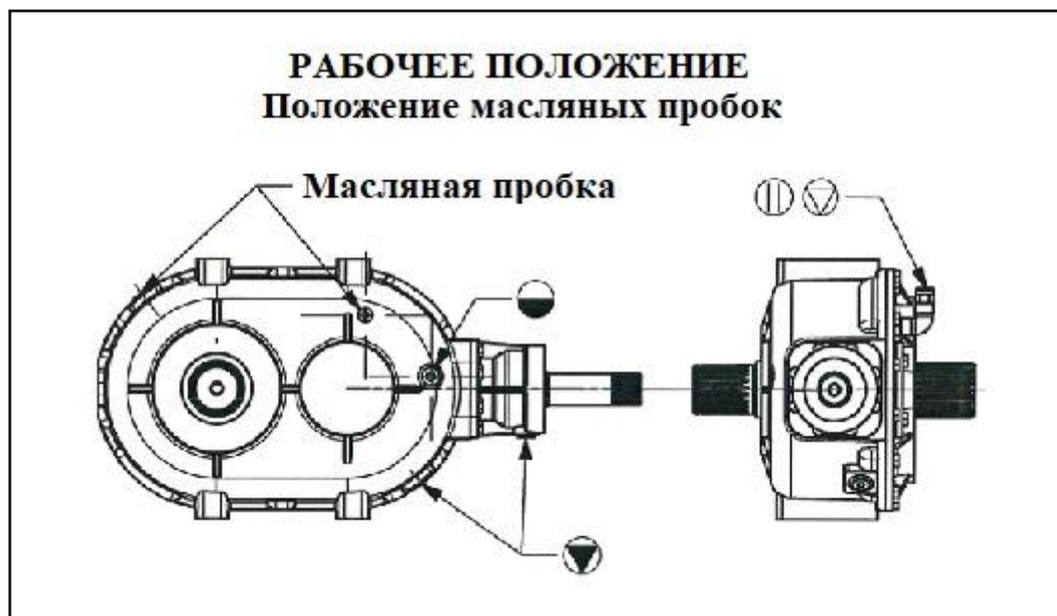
Схема заливки и контроля масла в редукторе
